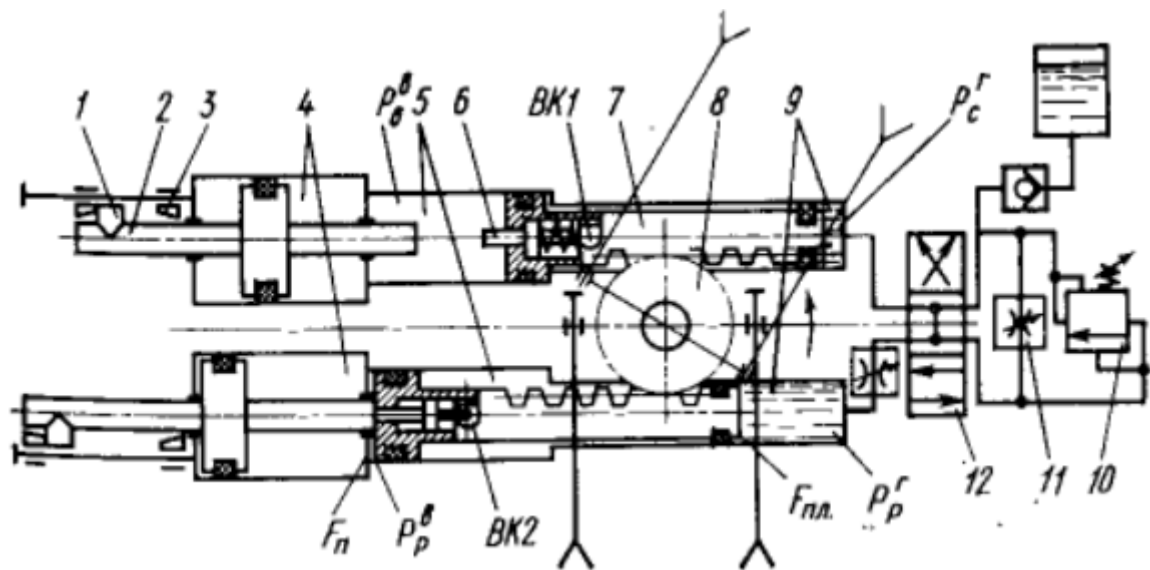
Схема механізму повороту робота «Циклон-3Б»: 1 – планка; 2, 7 – шток; 3 – гайка-упор; 4 – пневмоциліндр упорів; 5 – робочий пневмоциліндр; 6 – прапорець; 8 – консоль; 9 – гідроциліндр; 10 – напірний клапан; 11 – дросель; 12 – гідралічний розподільник.[1]
